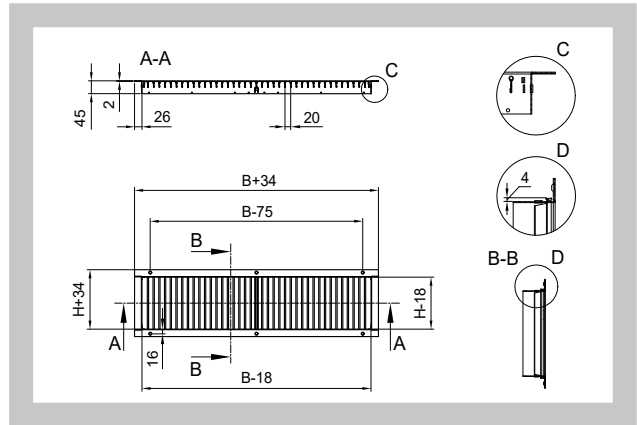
Einstellbare Lamellen horizontal - zweireihig
